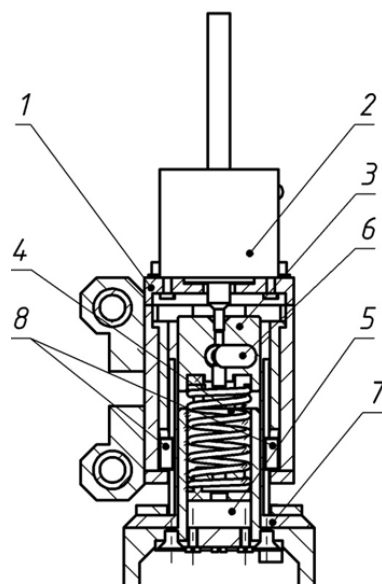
Конструкция стоек акустического и вихретокового контроля: 1 – корпус; 2 – линейный актуатор; 3 – втулка; 4 – пружина; 5 – тензометрический датчик; 6 – штифт; – пружина; 7 – шток; 8 – направляющие сухари
